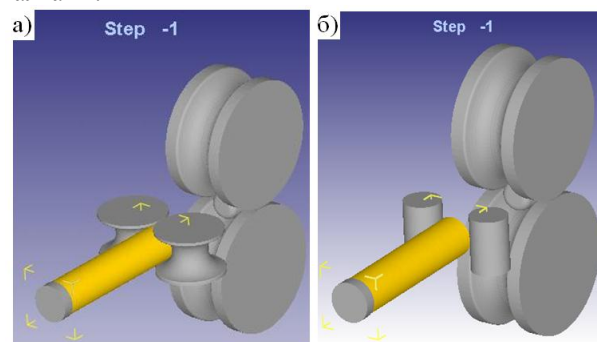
3D-модель стана продольной прокатки труб с ручьевыми (а) и цилиндрическими (б) эджерными валками
